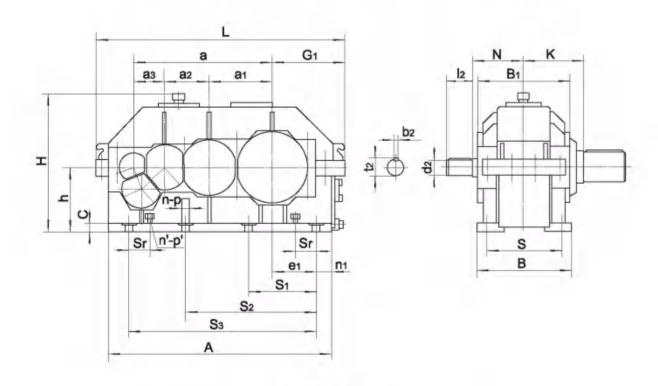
QY34D减速器外形尺寸 Figure 11 External dimension of QY34D decelerator
